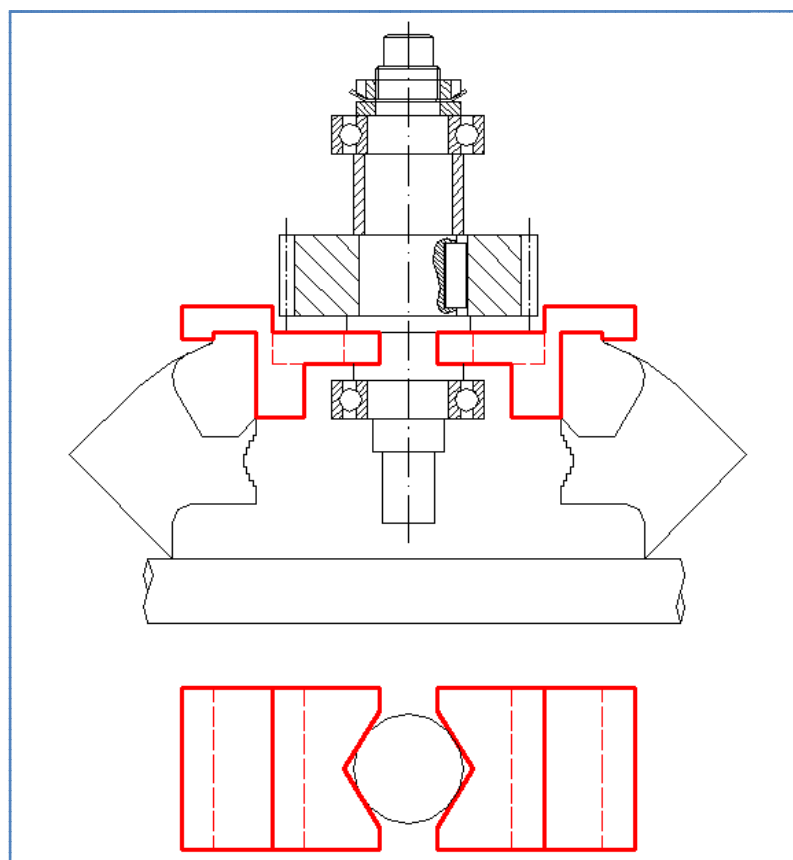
Alzado y planta ilustrativas de cómo quedaría el eje amarrado con los soportes
